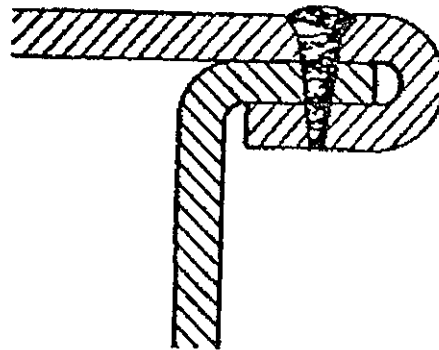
Soldadura de láser de simple sello de candado.
